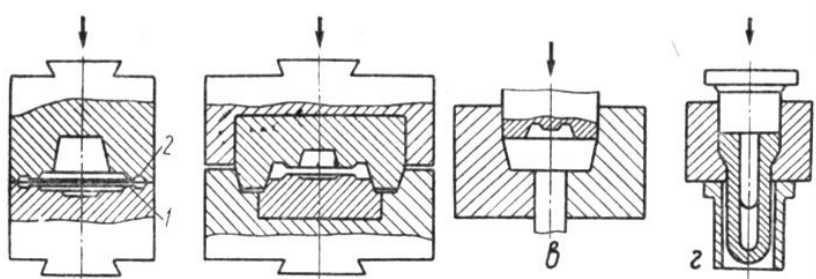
Схемы горячей объемной штамповки и заготовительных ручьев
